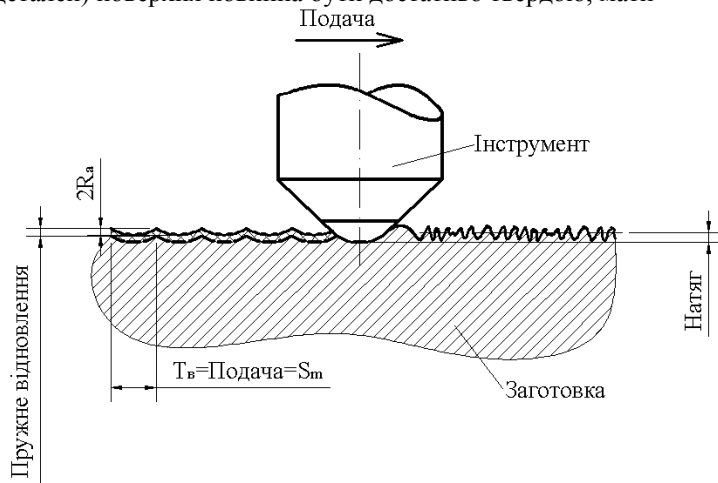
Схема зміцнювально-вигладжувального оброблення
